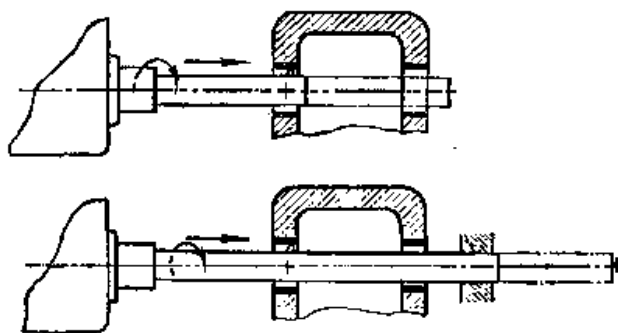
Схема розточування без кондуктора з подачею шпинделя
